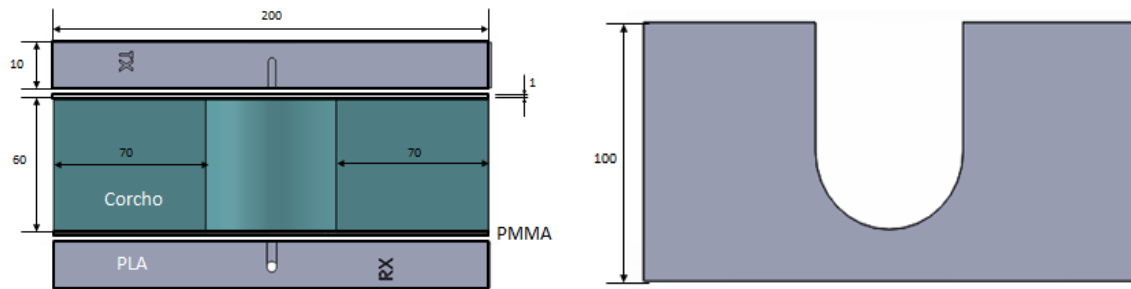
Dimensiones de la celda de medida en alzada y planta.
